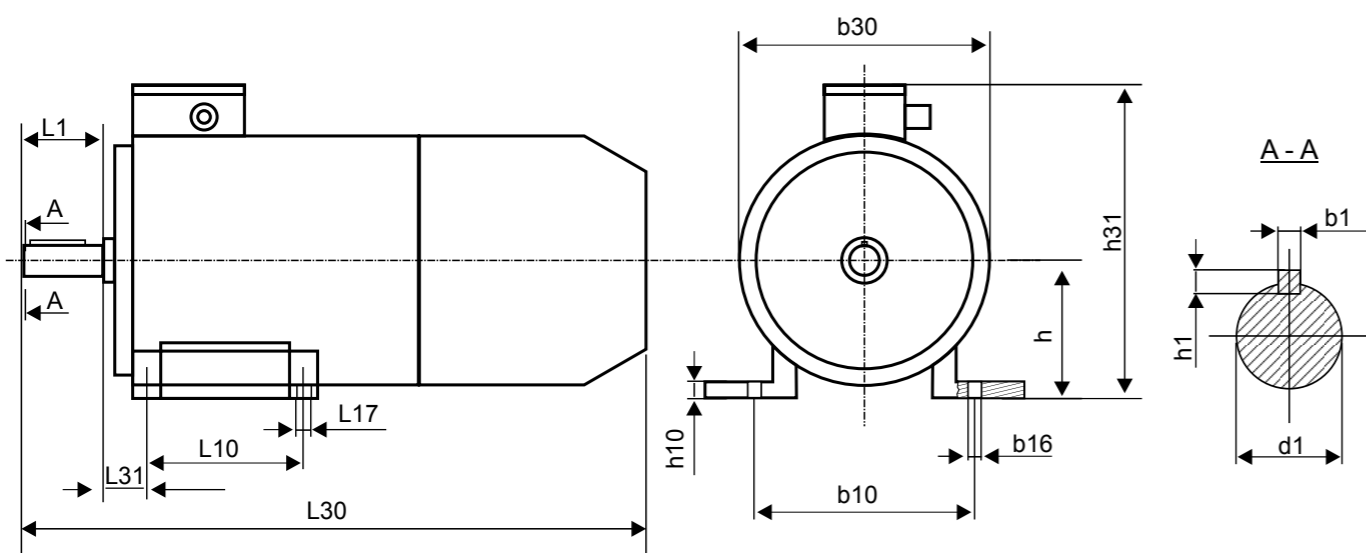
Габаритные и установочно-присоединительные размеры (IM1001)
